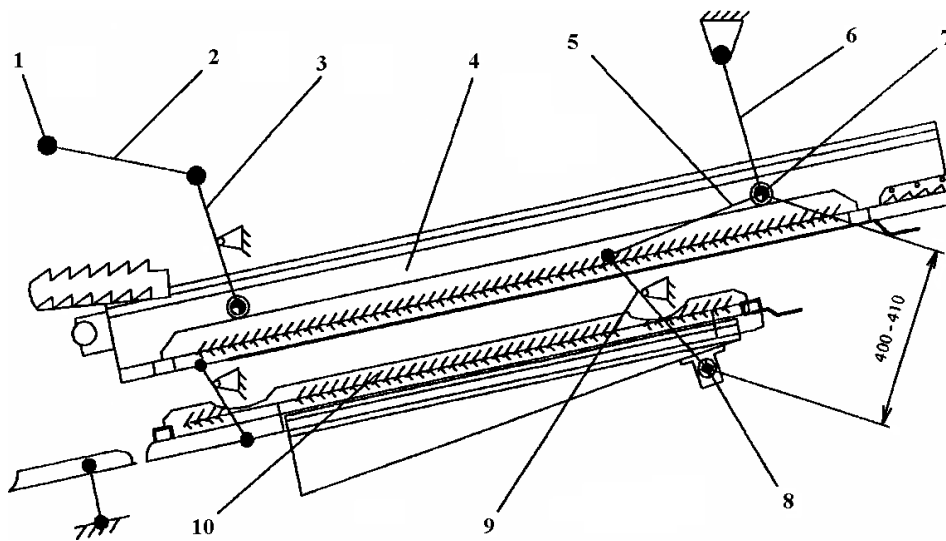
Механізм коливання решіт: 1 – опорні підшипники коливального вала; 2 – шатун; 3 – приводний важіль; 4 – верхнє решето; 5, 6 – підвіска; 7 – задня вісь кочення верхнього решета; 8 – нерухома вісь кочення важелів решіт; 9 – двоплечий важіль; 10 – нижнє решето
